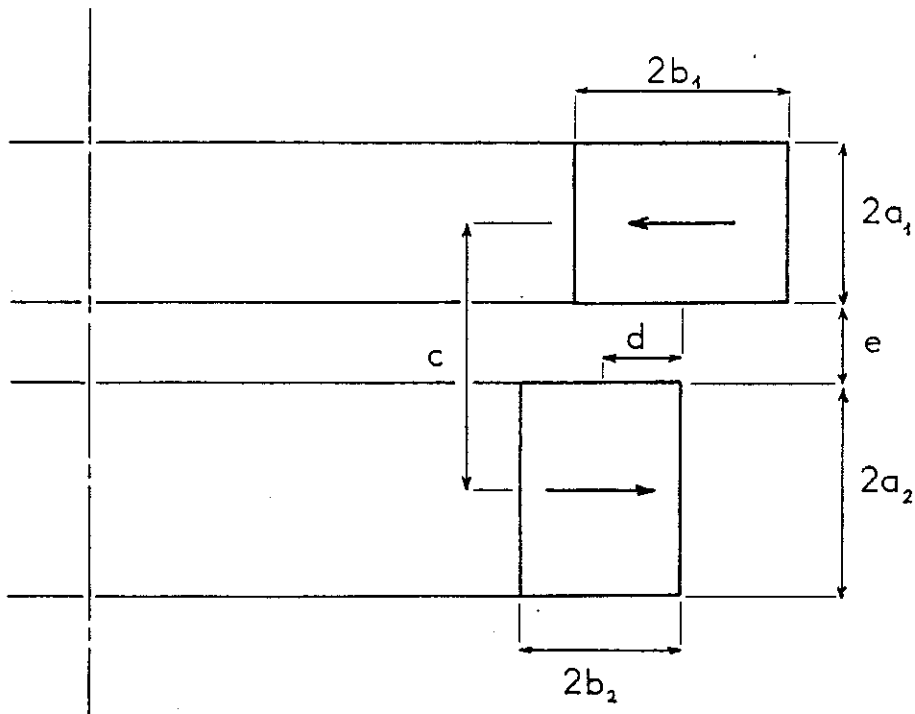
Palier magnétique de type E ; Définition des dimensions
